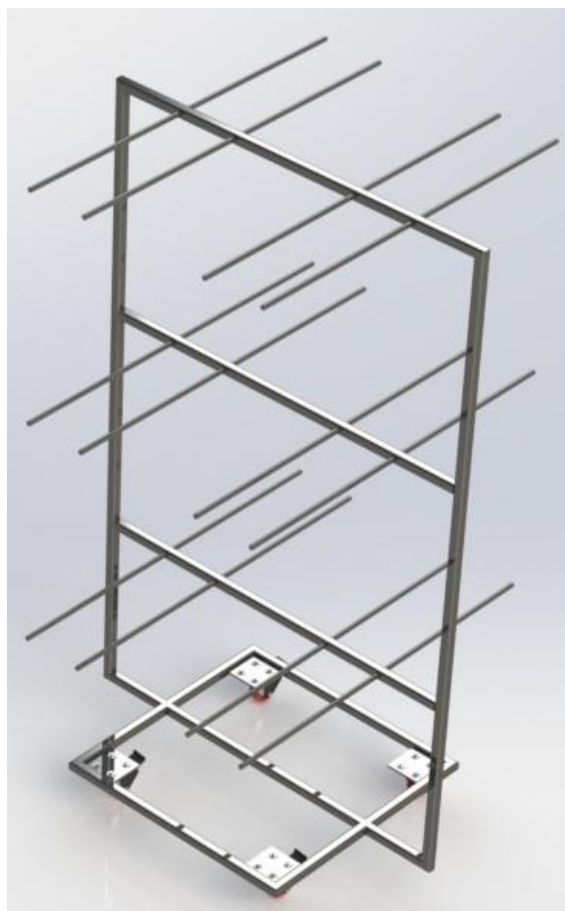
Esboço da estrutura metálica para paletização dos painéis de porta.
